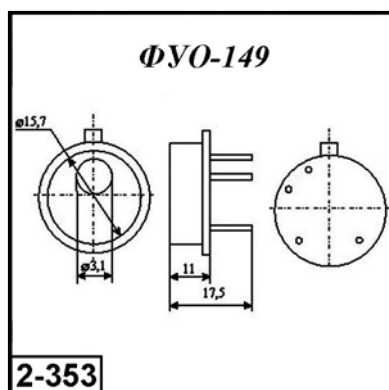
Внешний вид и габаритные размеры ФПУ ФУО-149
